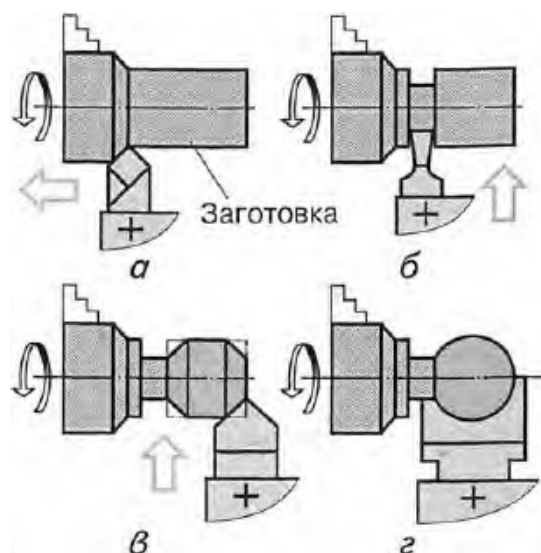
ПОСЛІДОВНІСТЬ ОБРОБКИ СФЕРИЧНОЇ ПОВЕРХНІ
